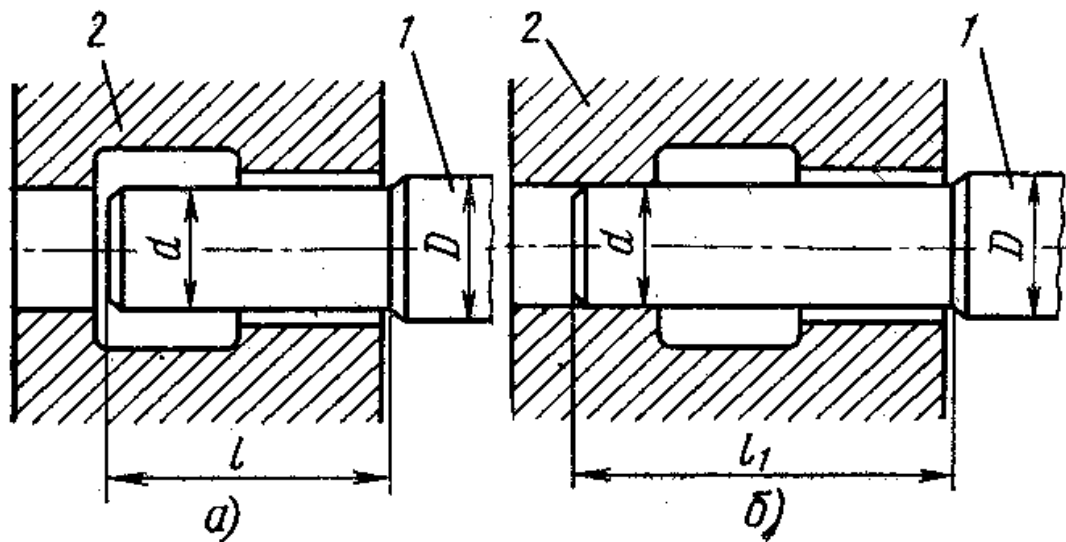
Схема складання ступеневого вала з корпусом:
